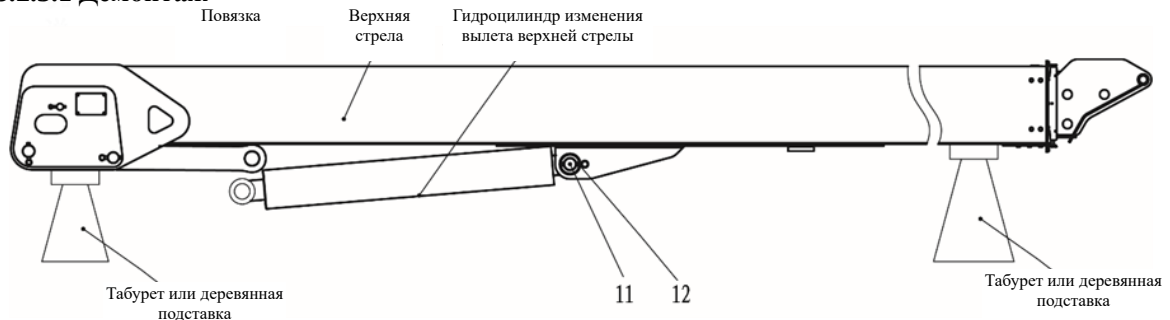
Схема разборки цилиндра подъема вылета верхней стрелы
